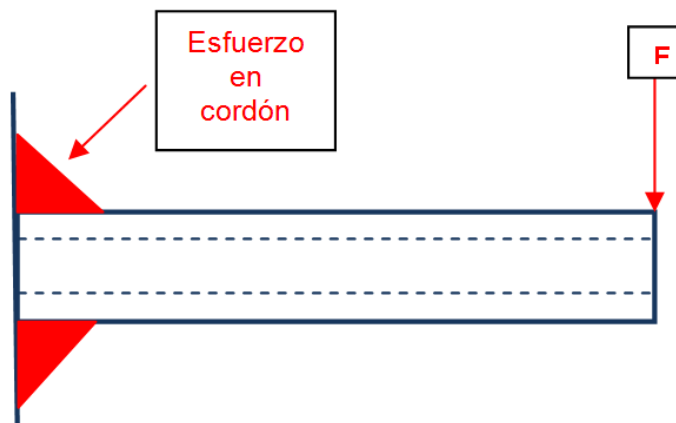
Esfuerzo en pieza tubular soldada.
